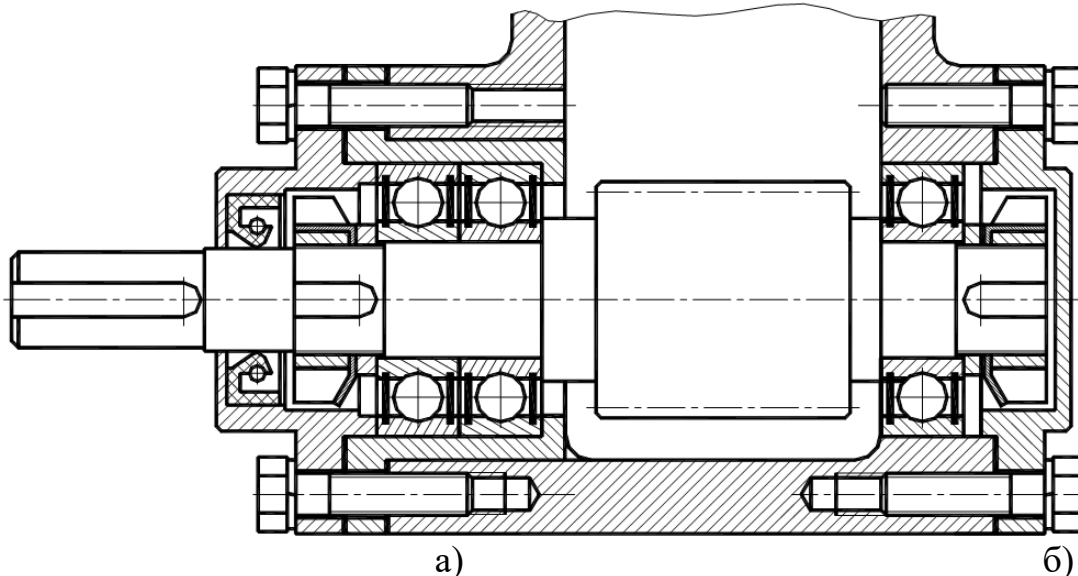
Установка вала на сдвоенных радиально-упорных шариковых подшипниках (а) и плавающем радиальном шариковом подшипнике (б)
